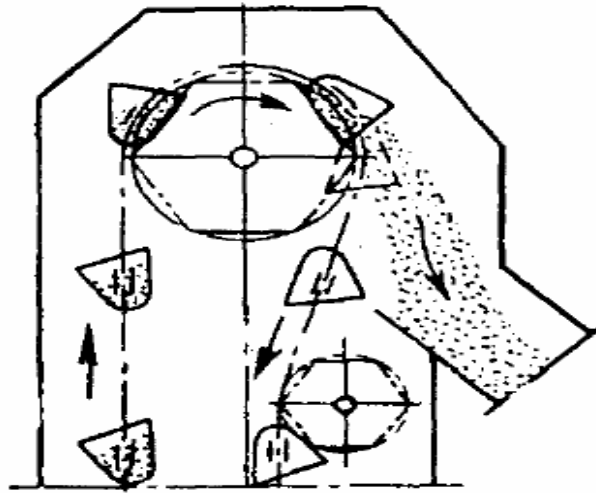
Malzemenin doğrudan beslenmesi [12].
